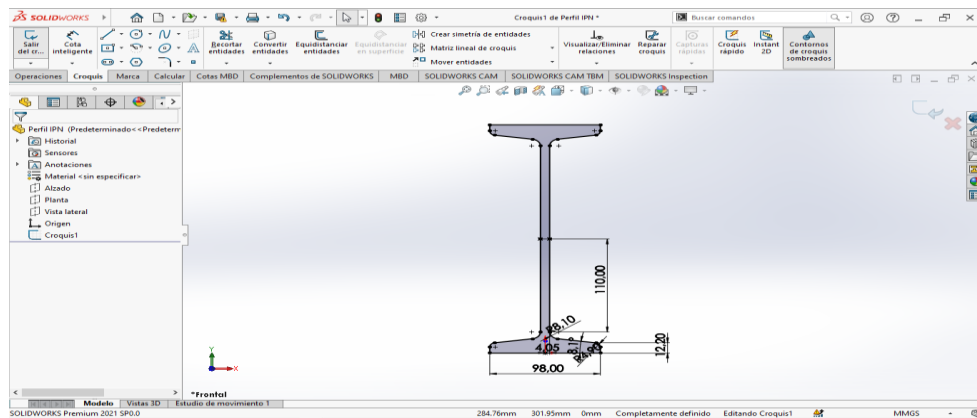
Croquis viga principal perfil IPN 220. Fuente: Autor
